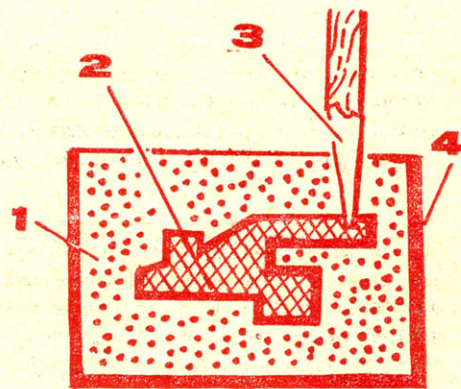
Неразборная форма: 1 — гипсовая заливка; 2 — парафиновая модель; 3 — установочный стержень (дерево); 4 — картонная коробка.
